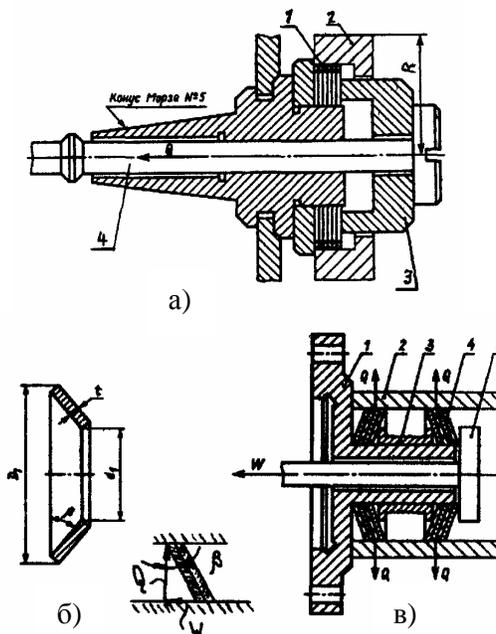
41 – Оправки с тарельчатыми пружинами ( а- с одним пакетом пружин; б – конструкция тарельчатой пружины; в- оправка с двумя пакетами пружин)
